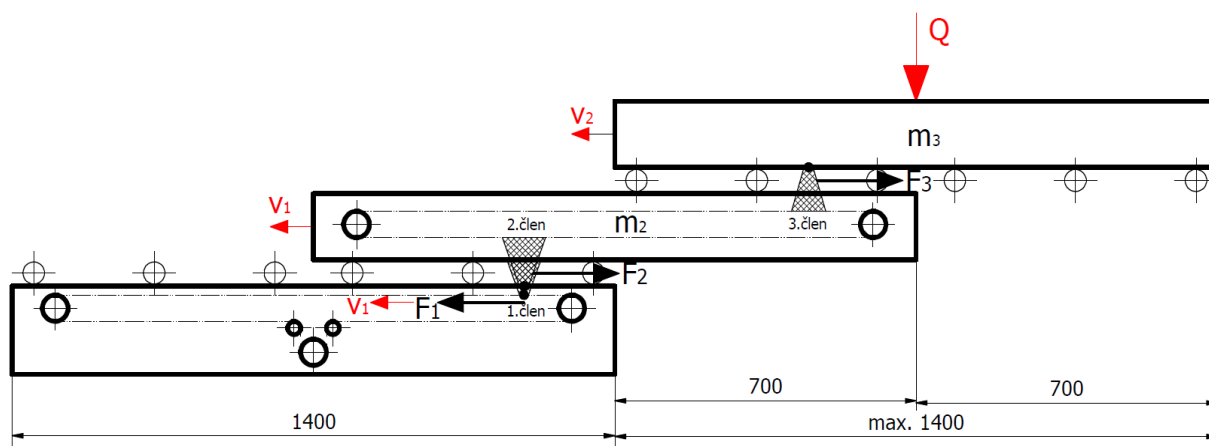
Rotační a posuvný pohyb mechanismu firmy AFB-GmbH [23]
